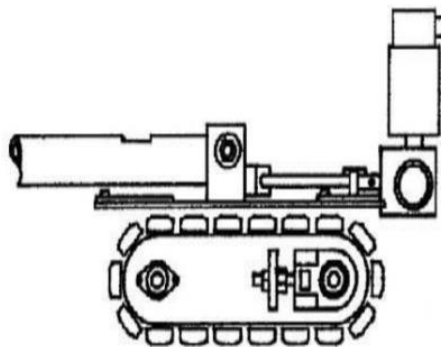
Внешний вид робота с цельной рабочей конструкцией
